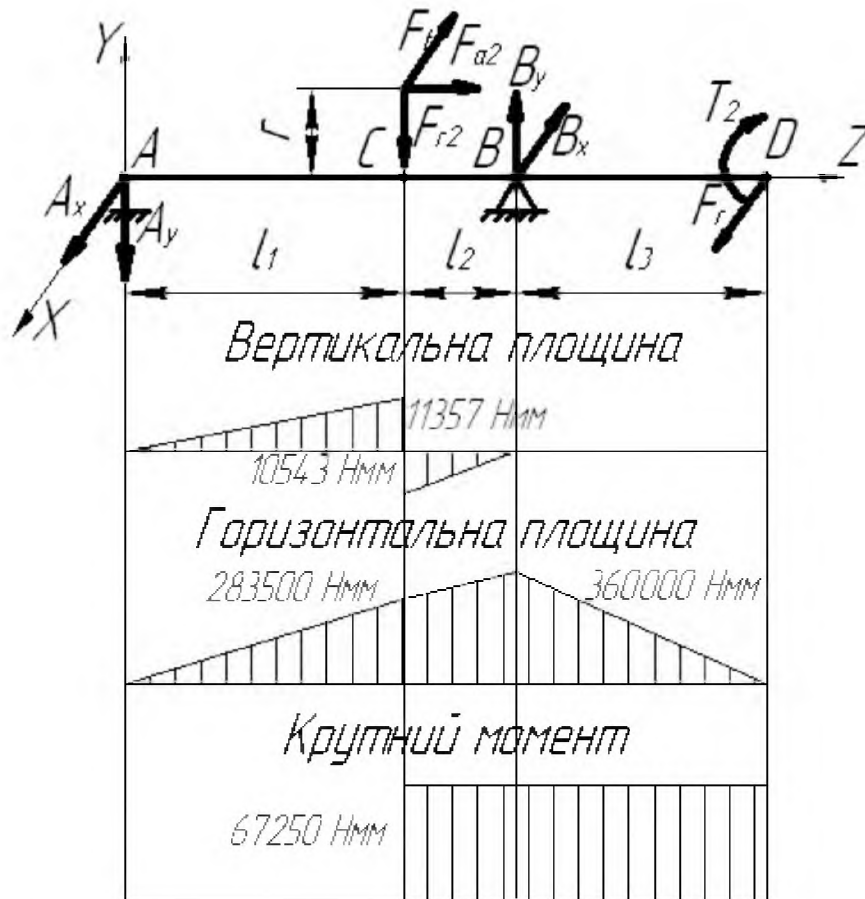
Схема до розрахунку вихідного вала конічного редуктора
